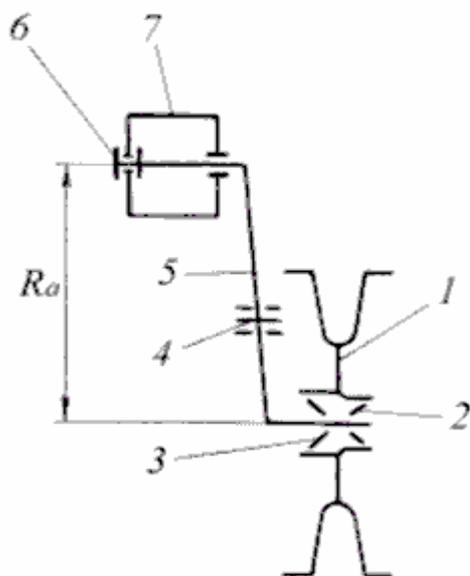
Схема установки направляющего колеса на кривошипе
